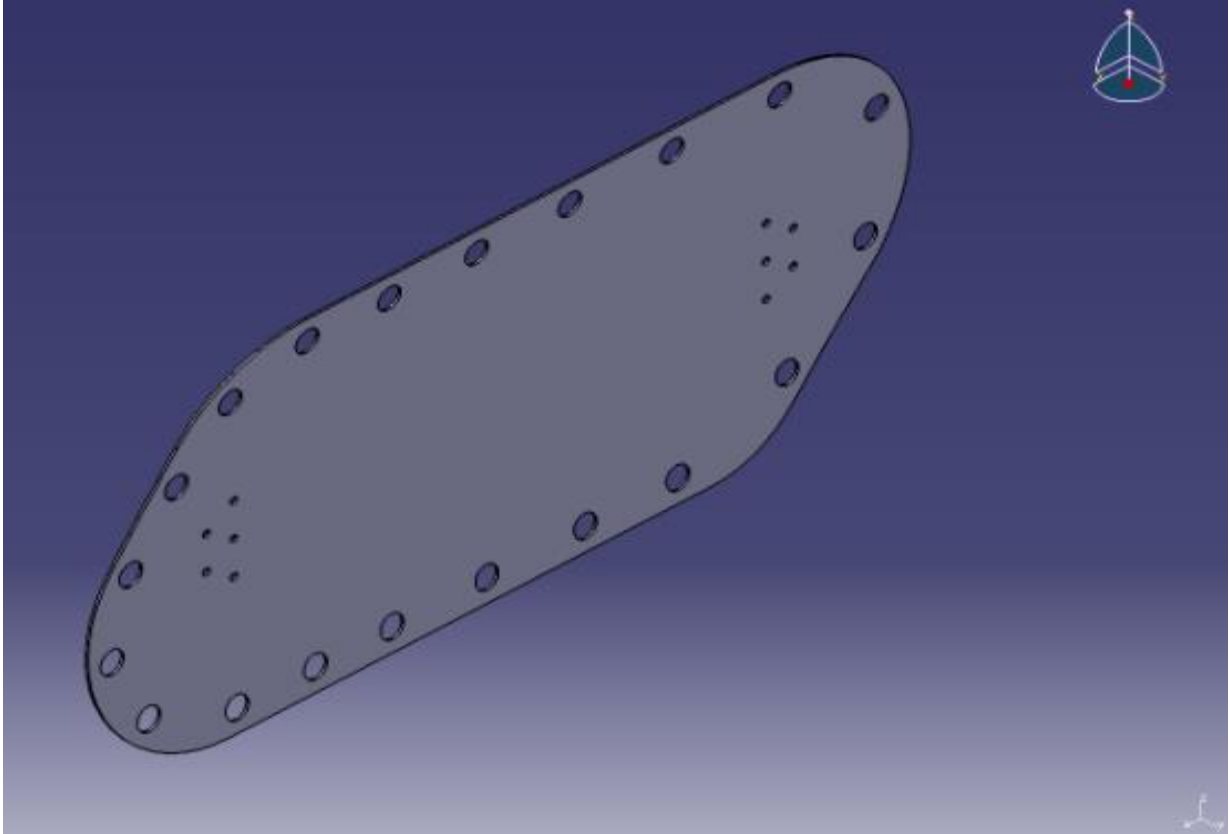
Tapa de inspección para material compuesto. Fuente: Propia del autor.
